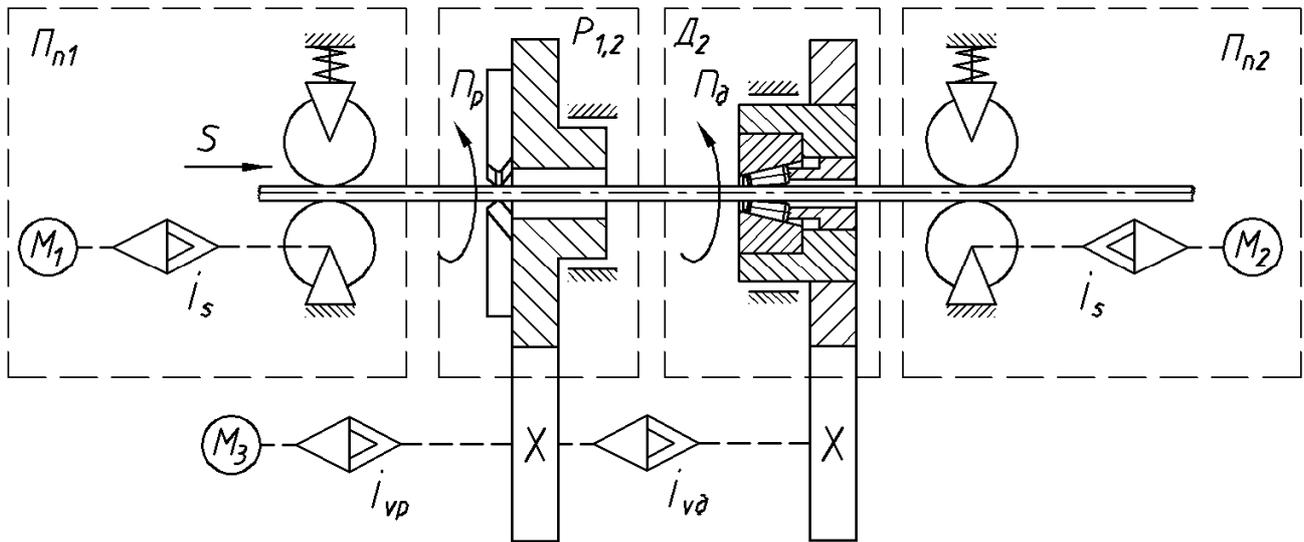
Конструктивная схема совмещенной обработки резанием и ППД роликами с продольно подаваемой заготовкой в сочетании с вращающейся резцовой головкой и обкатником
